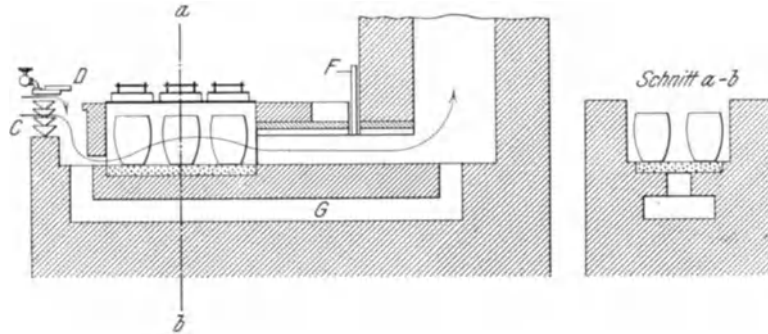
Tiegelofen der Sivyer Steel Casting Co.
